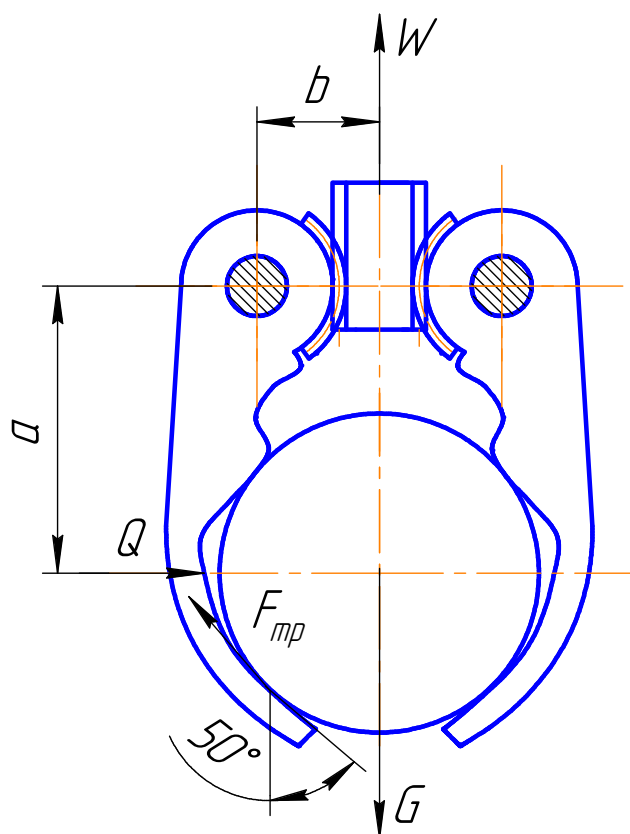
Расчетная схема рычажного механизма схвата
